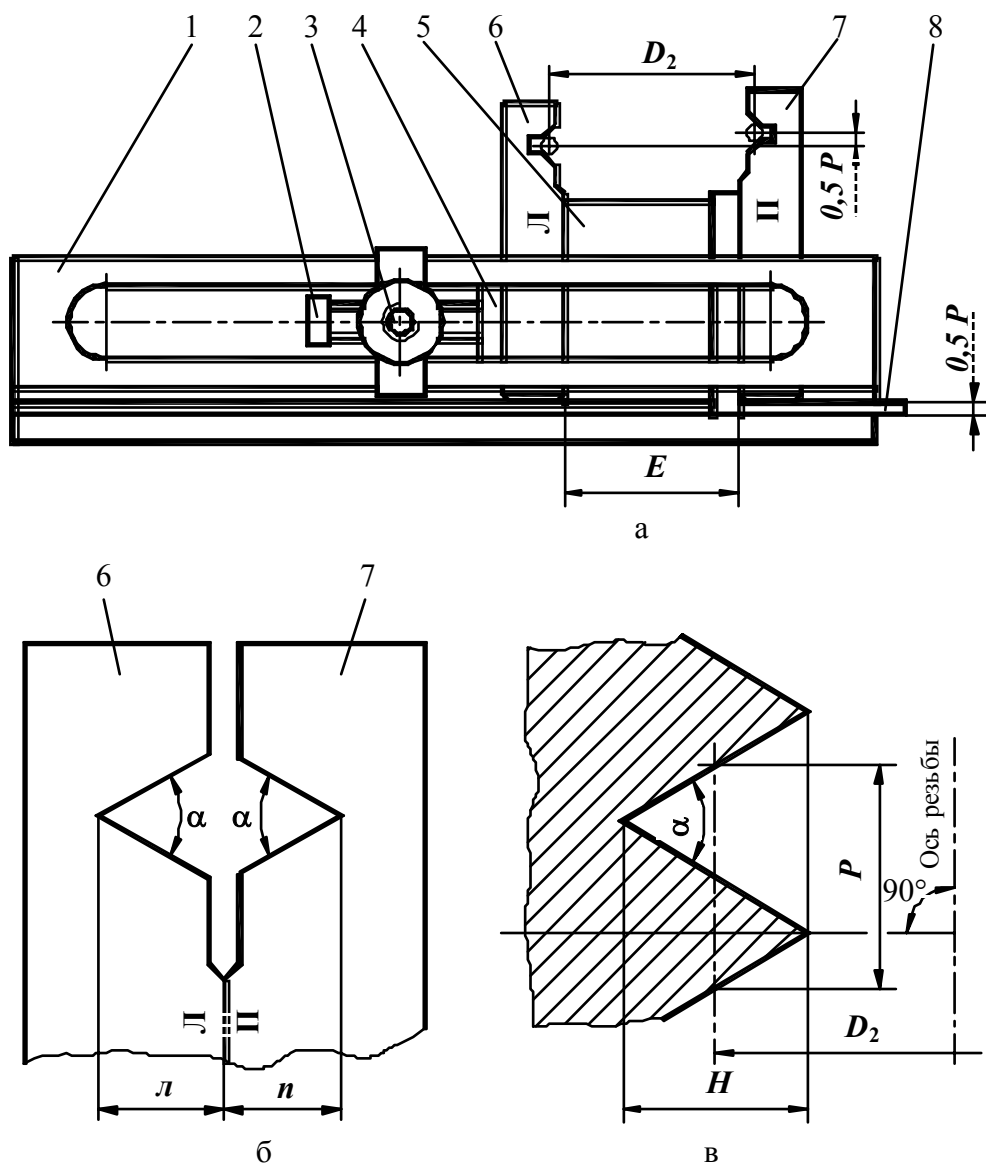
Схема наладки калибра для измерения среднего диаметра внутренней резьбы: а, б – калибр; в – номинальный профиль резьбы; 1 – державка; 2 – стопорный винт; 3 – зажимная гайка; 4 – планка прижимная; 5 – блок концевых мер; 6, 7 – левый и правый боковики; 8 – концевая мера
